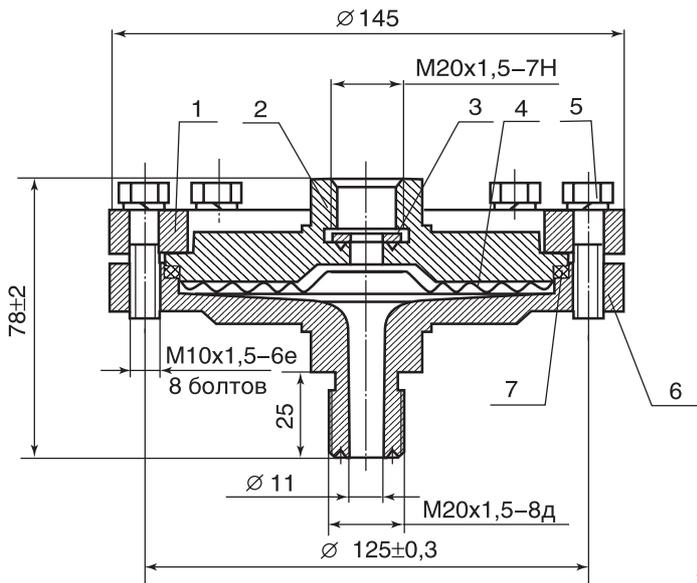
Разделитель мембранный РМ модели 5322. Габаритные и присоединительные размеры
